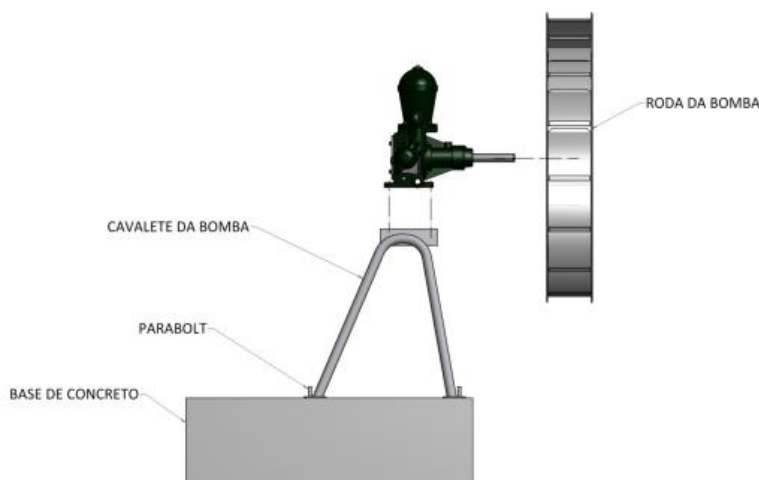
Recomendaciones básicas para el montaje del conjunto de bomba hidráulica ZM®.
